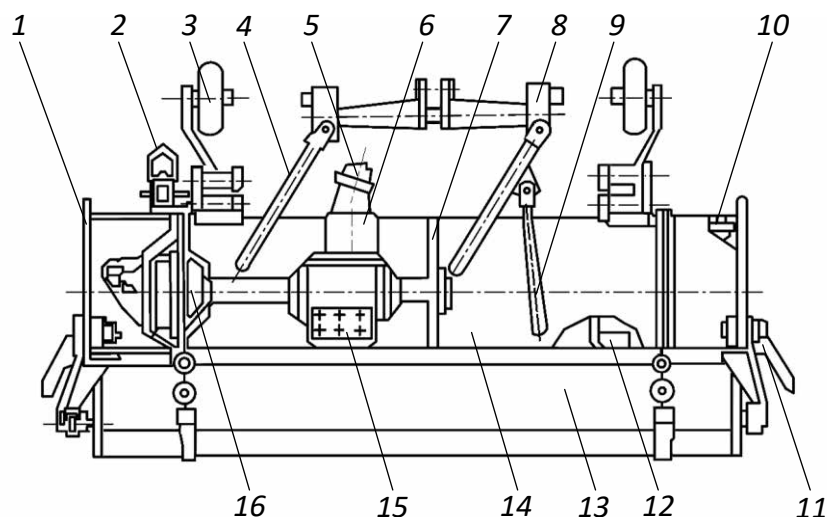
Фреза садова із змінною шириною захвату ФПШ – 200: 1 – рама знімна ліва; 2 – лапа розпушувальна; 3 – колесо опорне; 4 – пристрій для бічного виносу фрези; 5 – вал карданний; 6 – муфта запобіжна; 7 – рама; 8 – начіпний пристрій; 9 – штанга обмежувальна; 10 – рама знімна права; 11 – лапа стрілочаста; 12 – фрезерний барабан; 13 – кришка рухома; 14 – кожух; 15 – редуктор конічний; 16 – редуктор циліндричний
